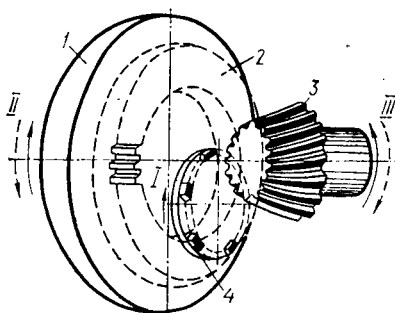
Схема нарезания конических колес с круговыми зубьями торцовыми зуборезными головками:
